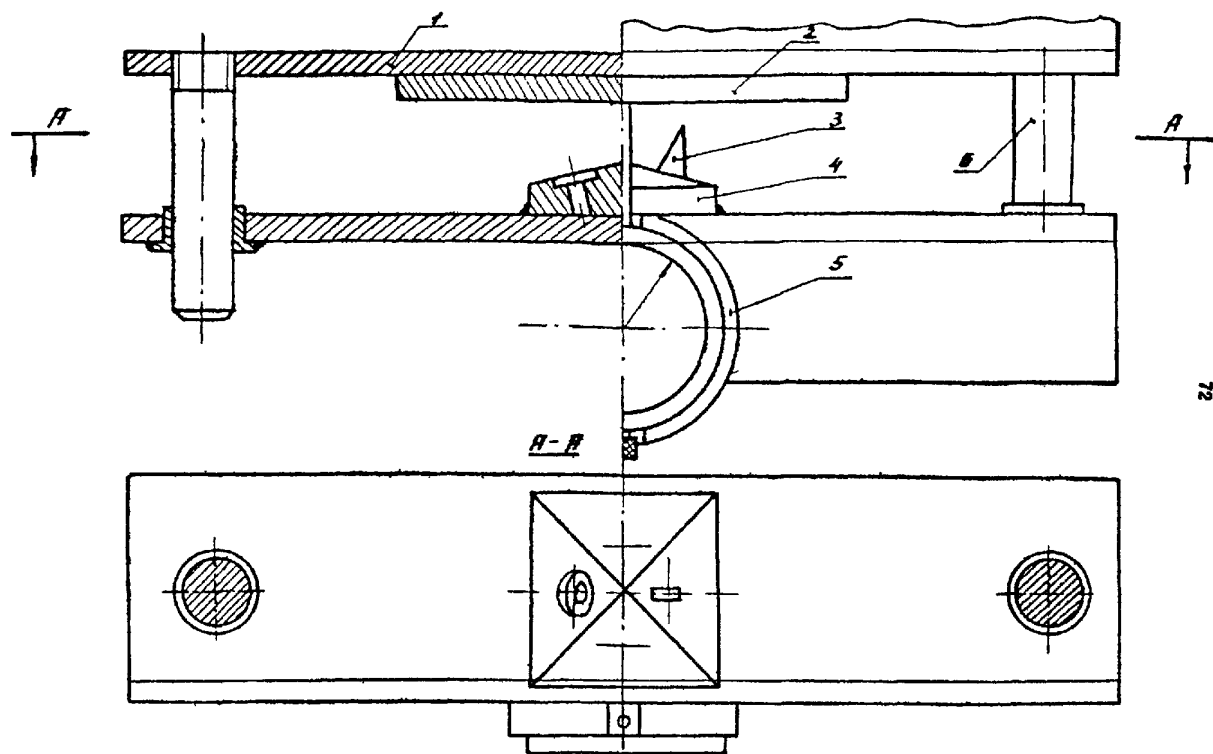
Устройство для нанесения зарубки способом вдавливания: 1 - уголок; 2 - образец; 3 - боек; 4 - патрон; 5 - оправка индикатора; 6 - направляющая.
